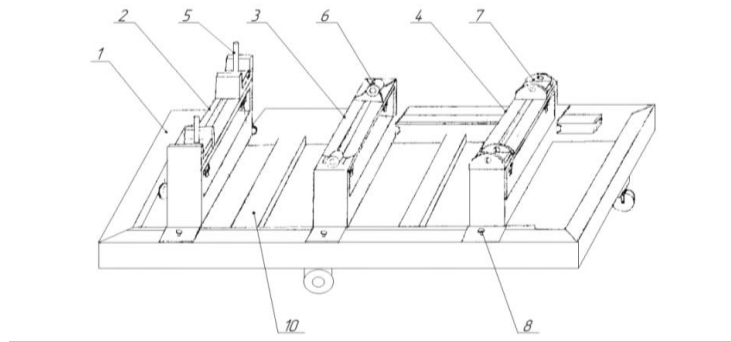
Универсальный стенд-кондуктор для разборки (сборки) кузовов автомобилей
